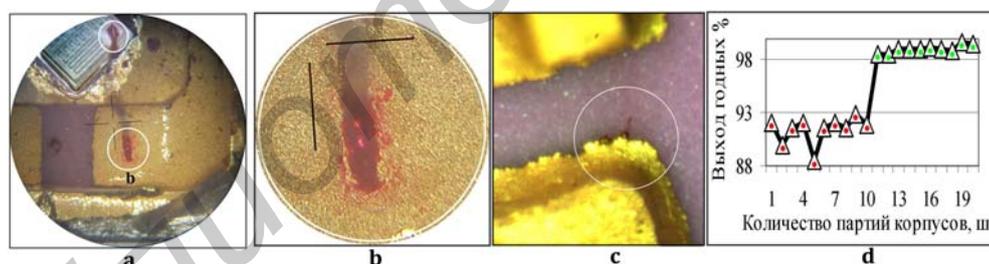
Выявление родамина в металлокерамическом соединении (а), (b – увеличено), (с) и динамика выхода годных по герметичности (d) для разного тока сварки (80 А для партий № 1-10 и 65А для партий № 11-20)
